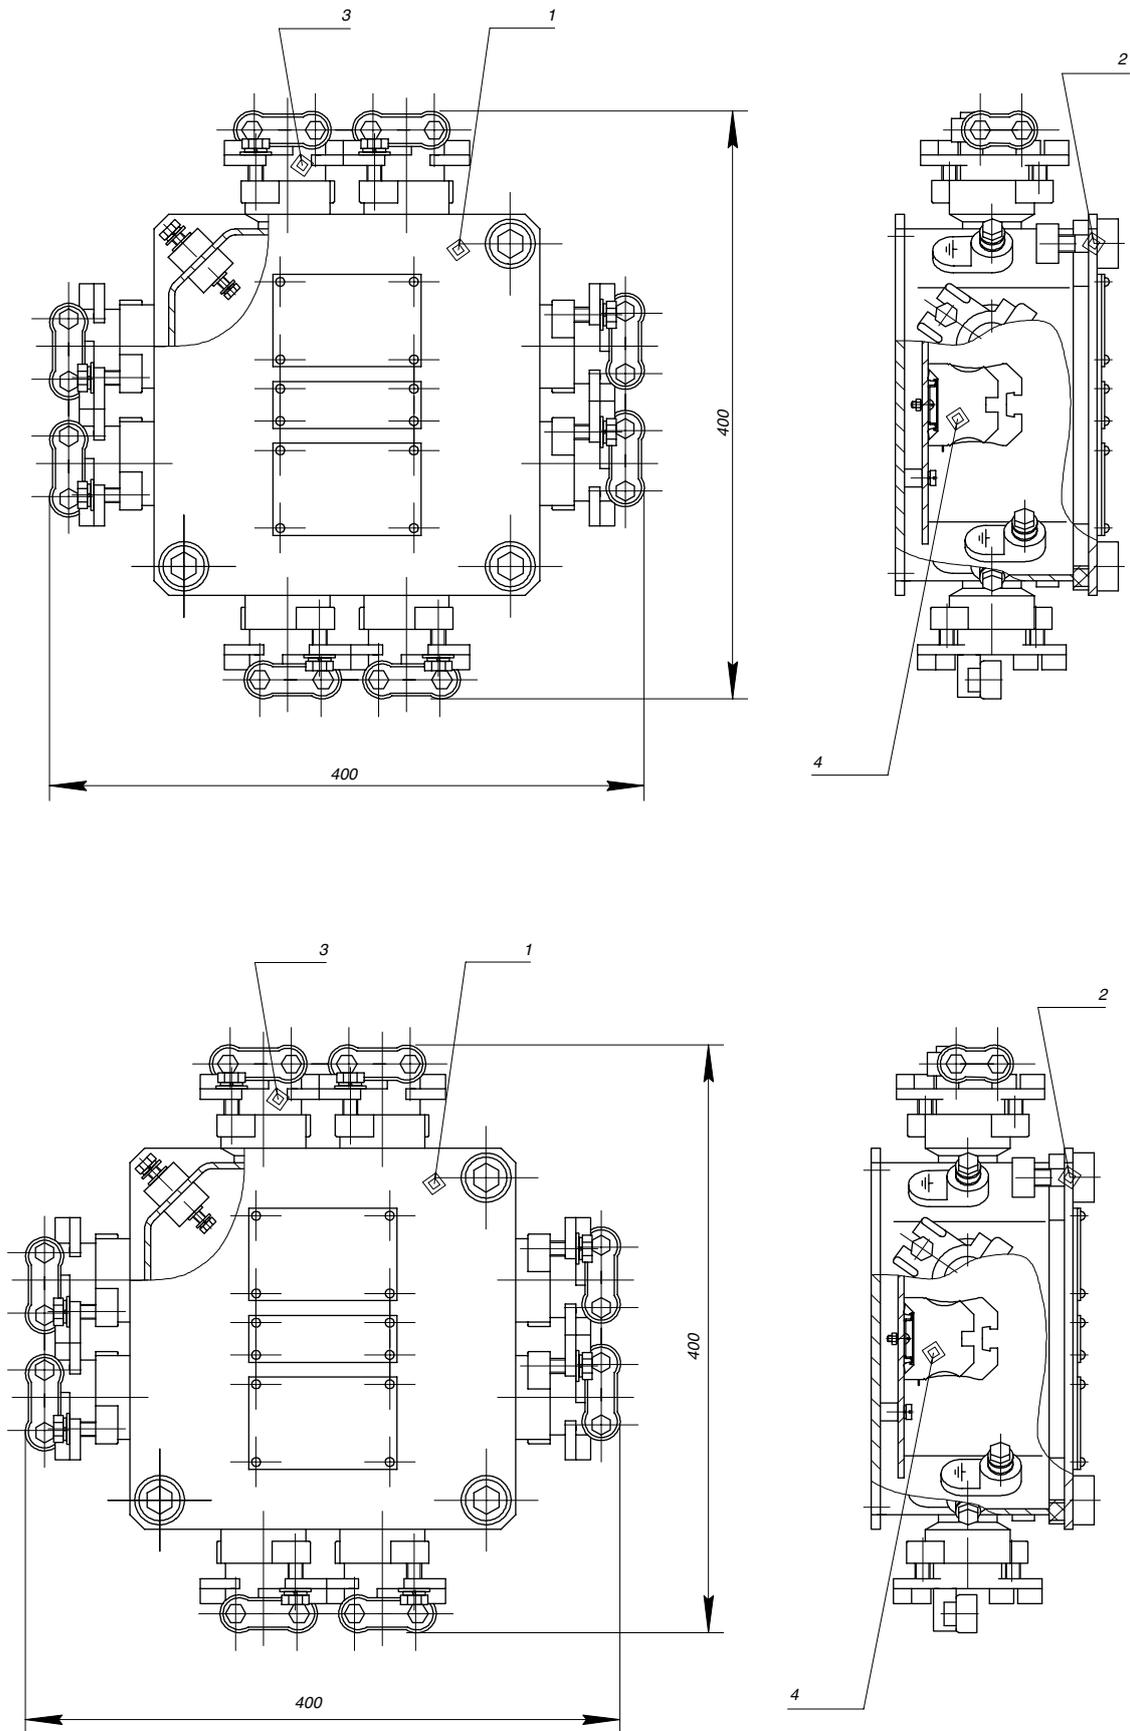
Общий вид и габаритные размеры (мм) устройств УСВН-1 и УСВН-2
